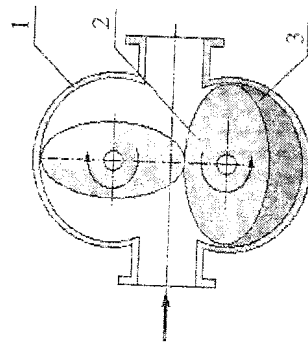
Счетчик жидкости с овальными шестернями: 1 — корпус; 2 — шестерня; 3 — измерительный объем
